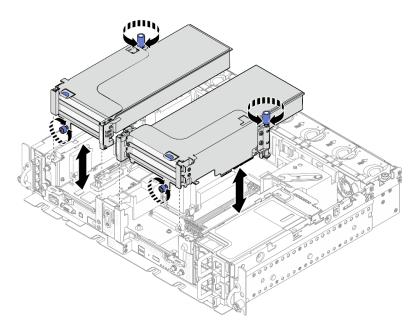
Removendo os conjuntos de placa riser PCle com adaptadores de comprimento integral
